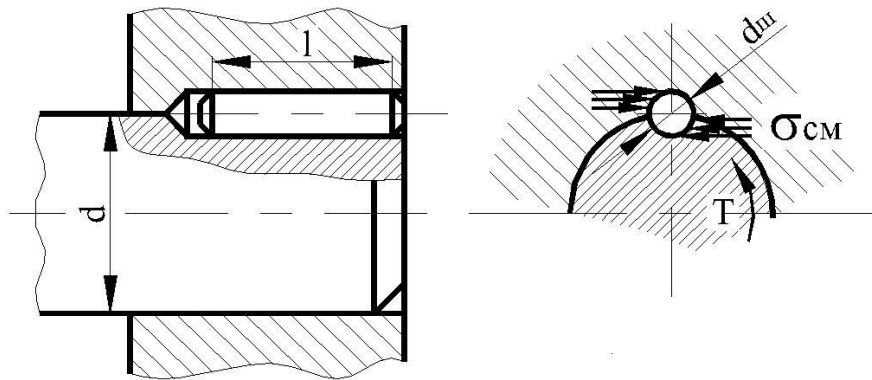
Розрахункова схема шпоноквого з'єднання циліндричною шпонкою
